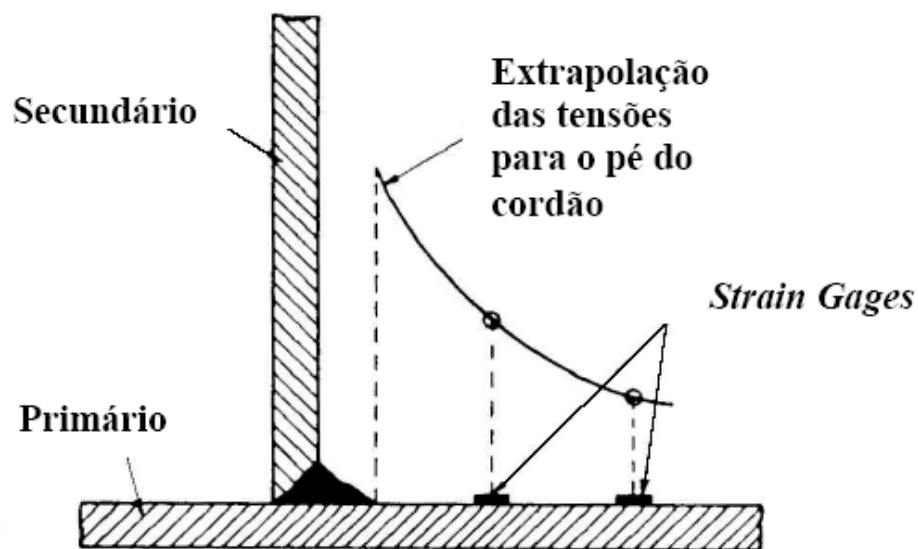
Extrapolação da tensão no pé do cordão de soldadura [17].
